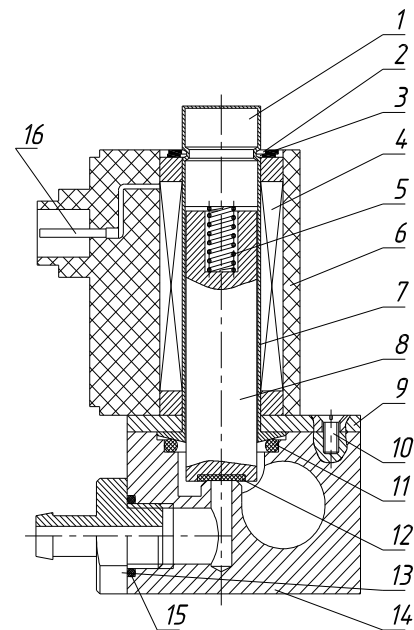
Поперечный разрез электромагнитного дозатора газа «DREAM»: 1 – неподвижный стержень корпуса-втулки; 2 – стопорное кольцо; 3 – плоская пружина; 4 – катушка электромагнита; 5 – возвратная пружина; 6 – пластмассовый корпус катушки; 7 – корпус-втулка; 8 – якорь электромагнита (клапан); 9 – пластина крепления корпуса-втулки к корпусу дозатора; 10 – крепежный винт; 11 – резиновое уплотнительное кольцо; 12 – резиновое плоское кольцо; 13 – расходный жиклер; 14 – корпус электромагнитного дозатора; 15 – резиновая уплотнительная шайба; 16 – контакты разъемного соединения
